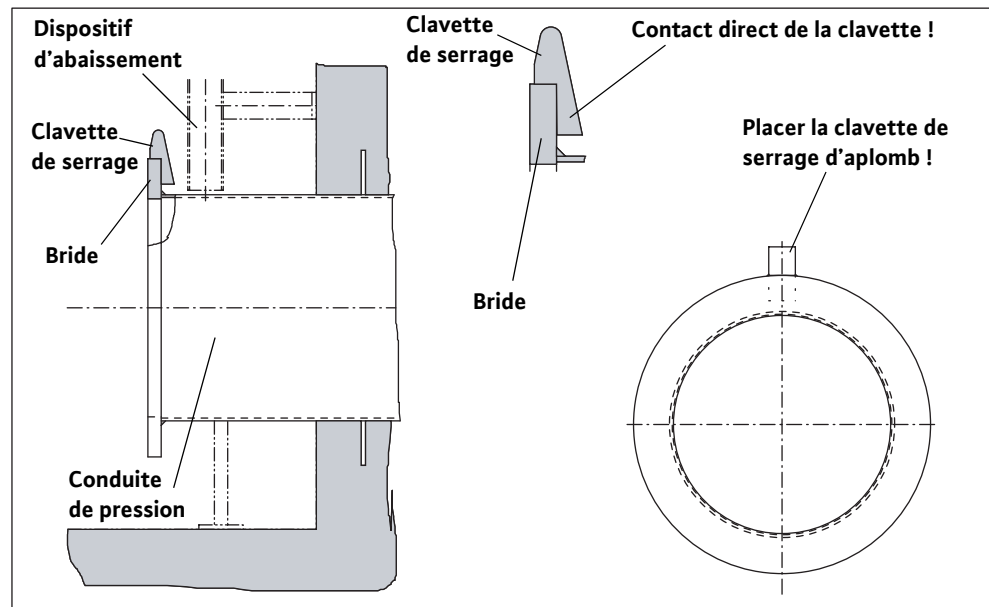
Montage sur la conduite de pression avec anneau en acier
